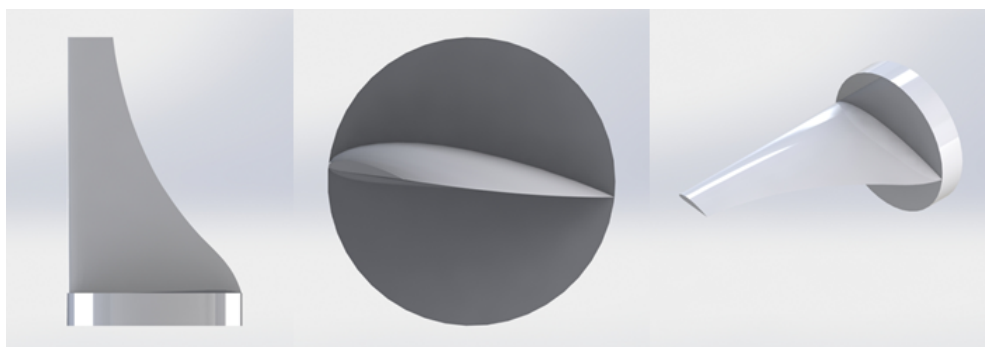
Várias vistas da pá final construída a partir do perfil NACA 4415.
